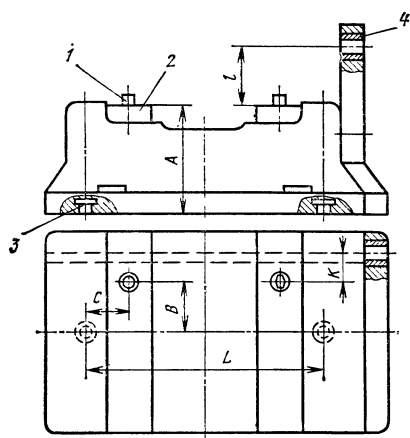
Основные размеры и схема базирования заготовки в спутнике по плоскости и двум отверстиям:
